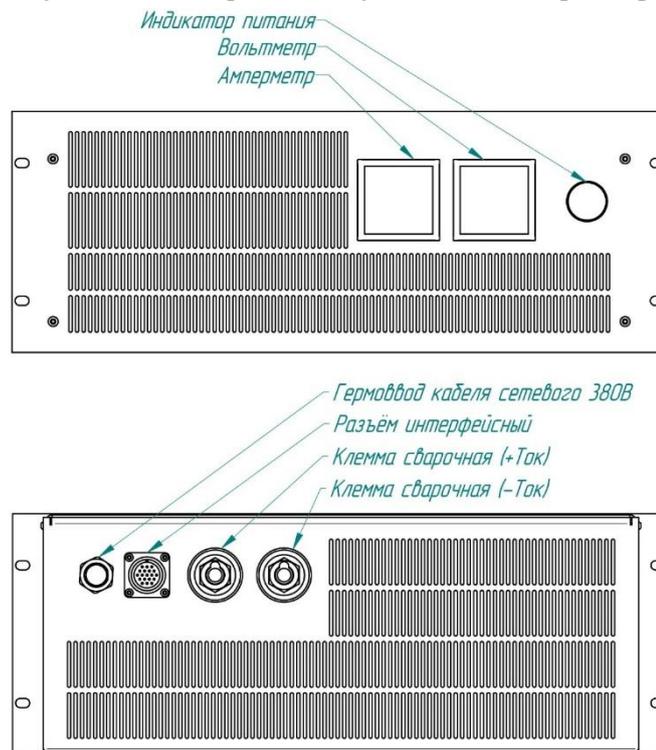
Описание индикаторов и разъёмов источника сварочного DC250
